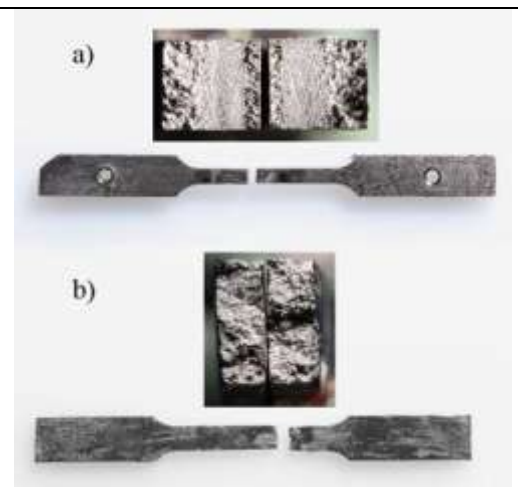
Fracturas de probetas soldadas a) e= 2 mm; b) e= 1 mm
